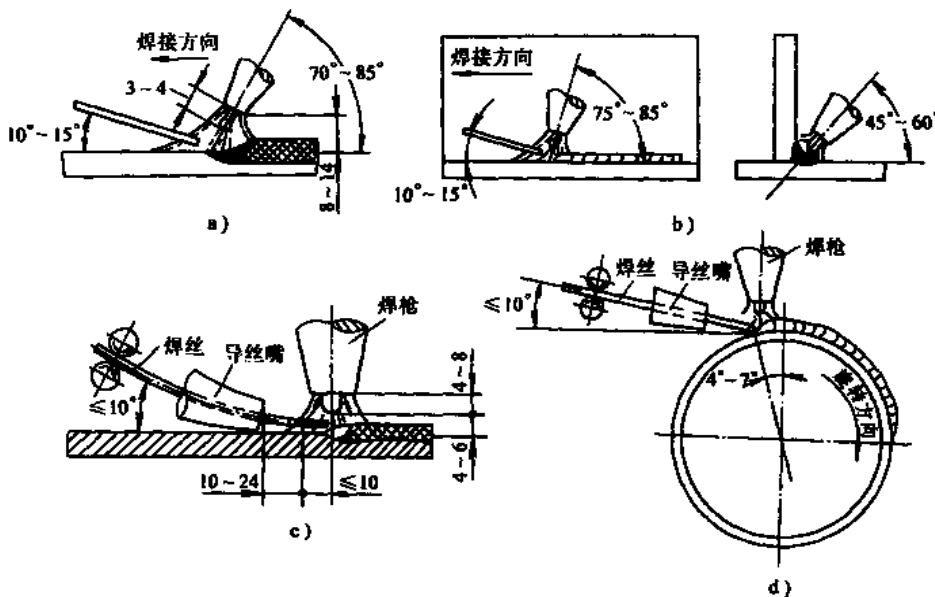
焊枪、填充焊丝和焊件之间正确的相对位置
